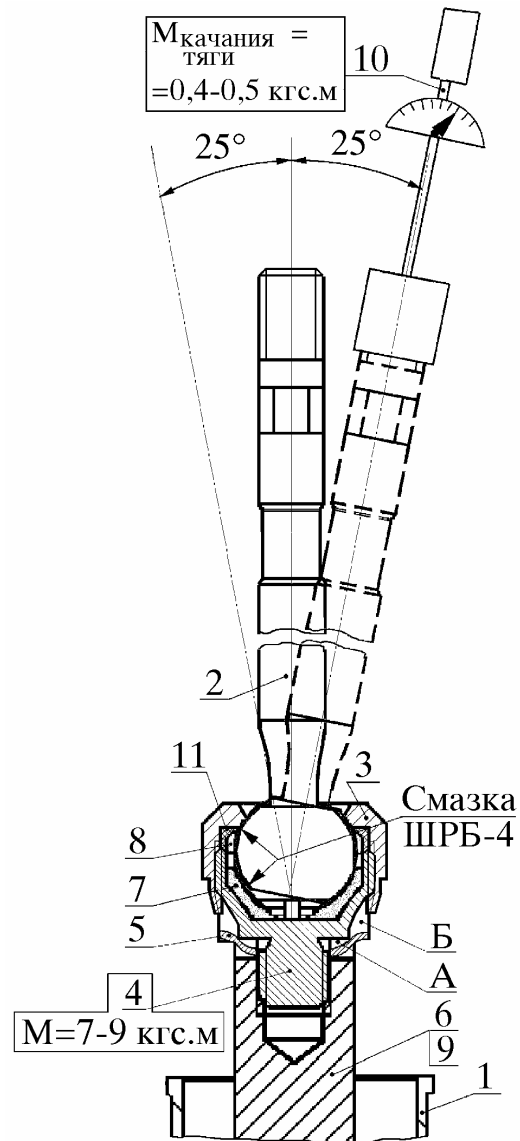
Установка корпуса шарнира и тяг с шарнирами на рулевой механизм:
